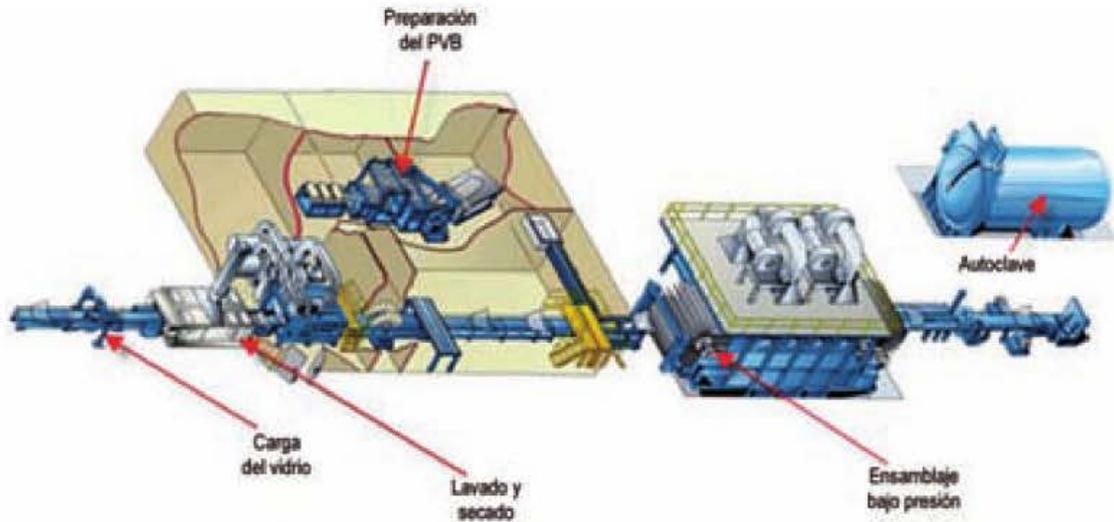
Fabricación del vidrio laminado. Ensamblaje.
